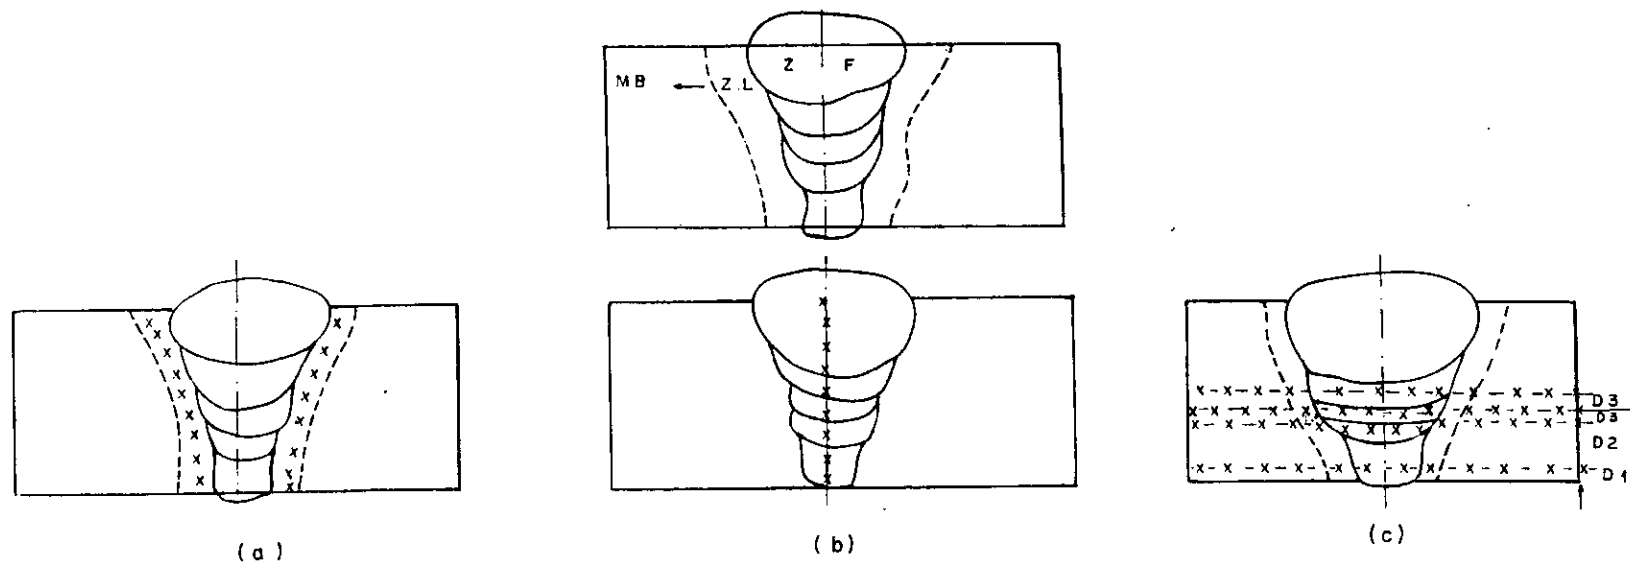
Techniques de filiations de la microdureté appliquées à un assemblage soudé en cinq passes.
